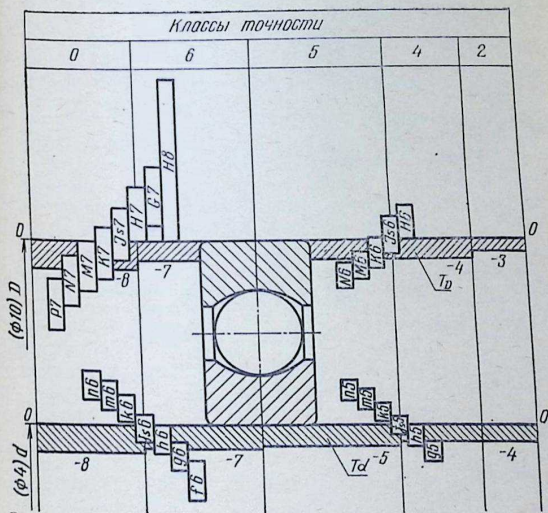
Схемы расположения полей допусков колец подшипника и сопрягаемых с ними деталей.
